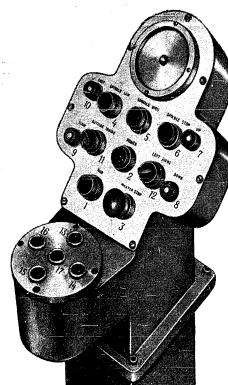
Радиально-фрезерный станок мод. Н-121 фирм
